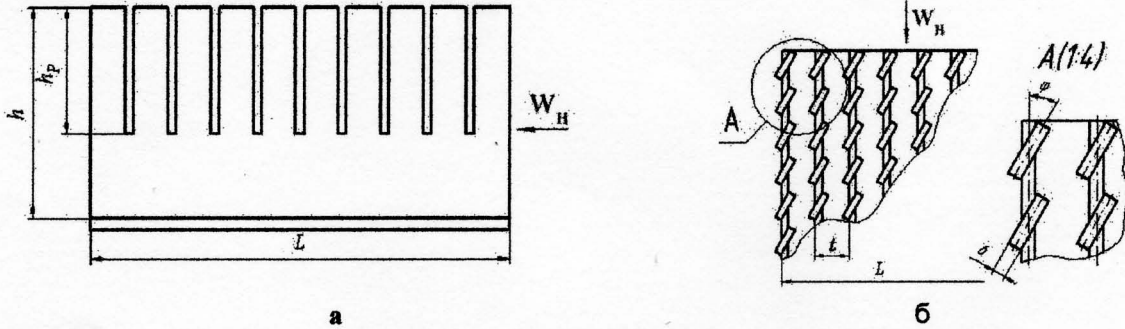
Конструкция пластинчато-просечного ребра: а – вид сбоку; б – вид сверху
